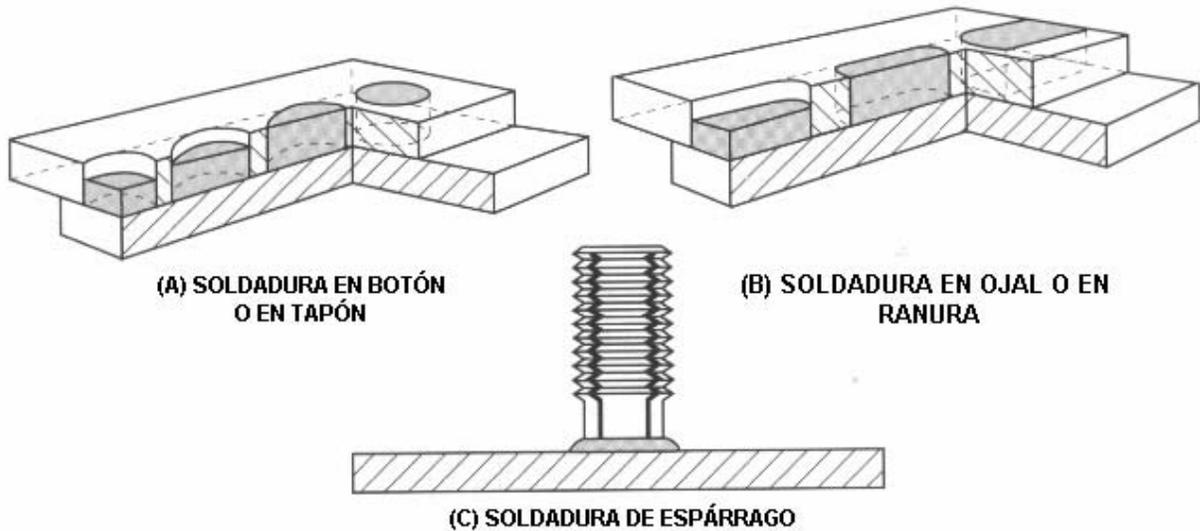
1 Soldaduras en tapón o en botón - en ranura o en ojal - de espárragos
